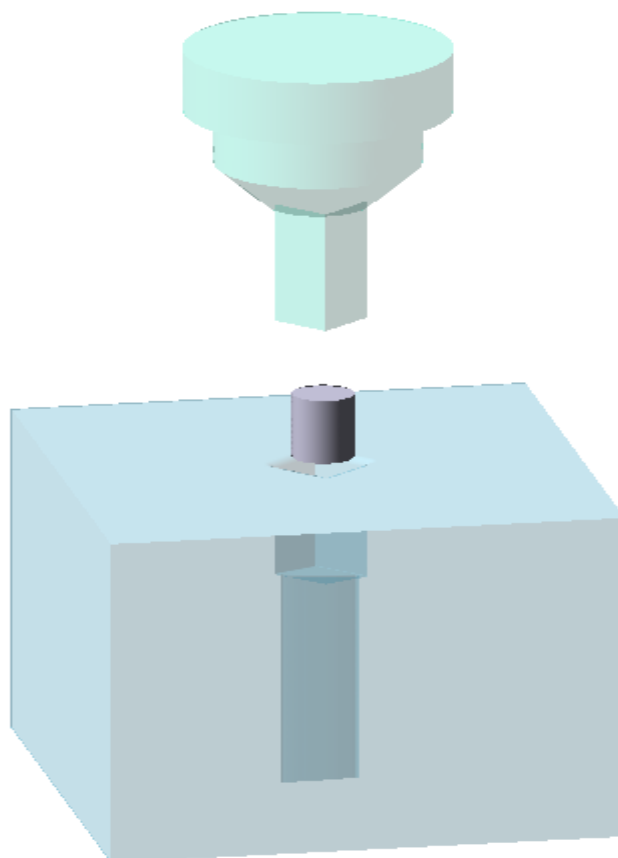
Збірна модель для процесу видавлювання заготовки з плоским торцем
